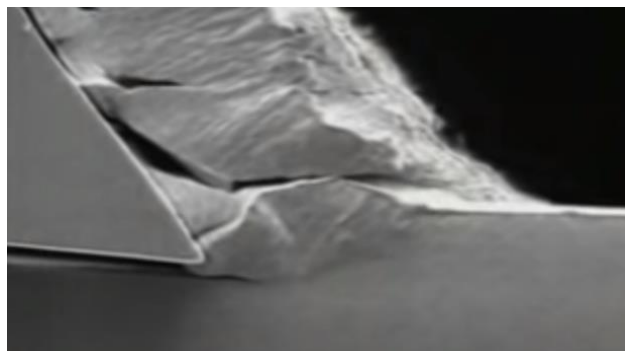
Fissuras na região de corte (adaptado de [13])
